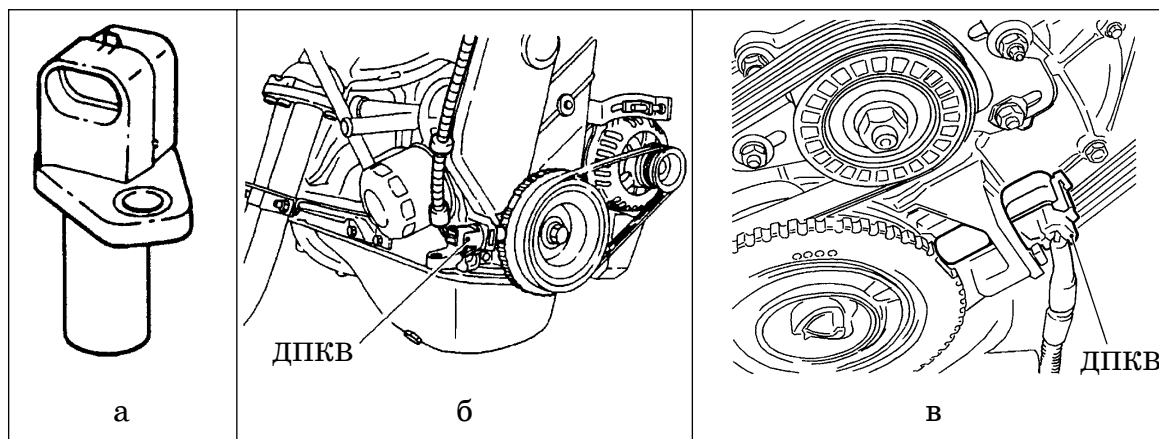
Внешний вид и расположение датчика положения коленчатого вала:
